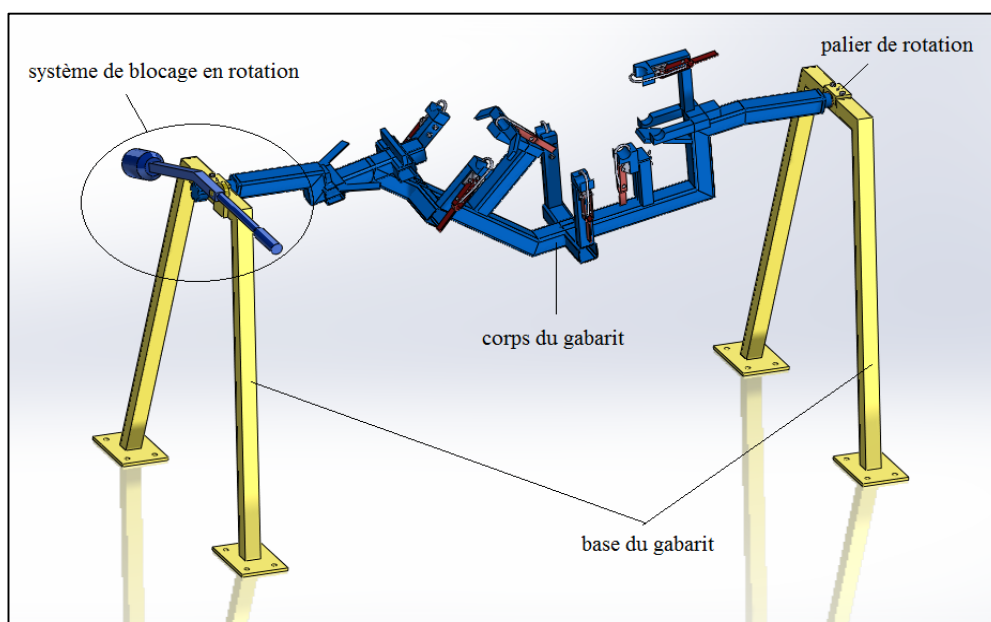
Gabarit de soudure du châssis Cuxi
